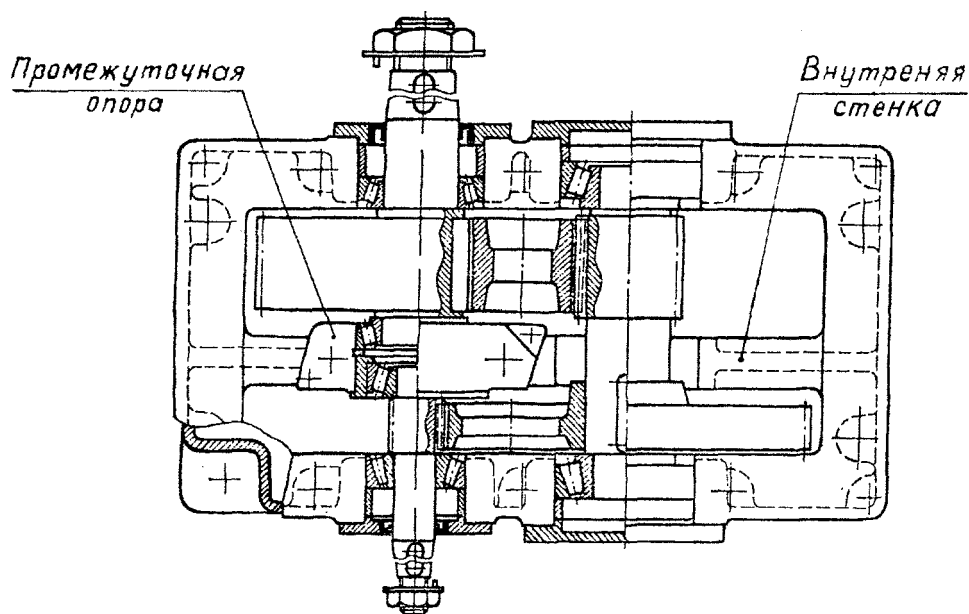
Двухступенчатый цилиндрический горизонтальный соосный редуктор с внутренней стенкой по всей длине корпуса
